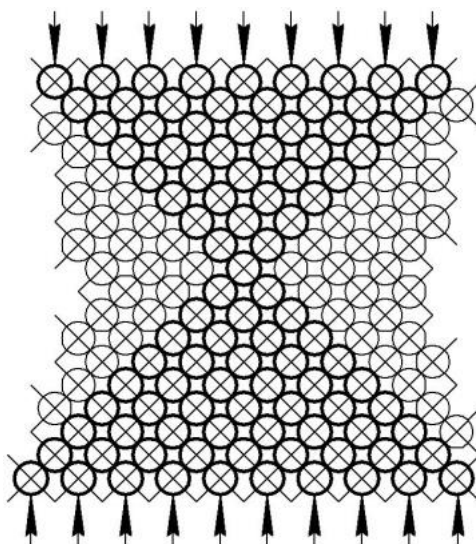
Схема осадки металла и образования конусов скольжения
